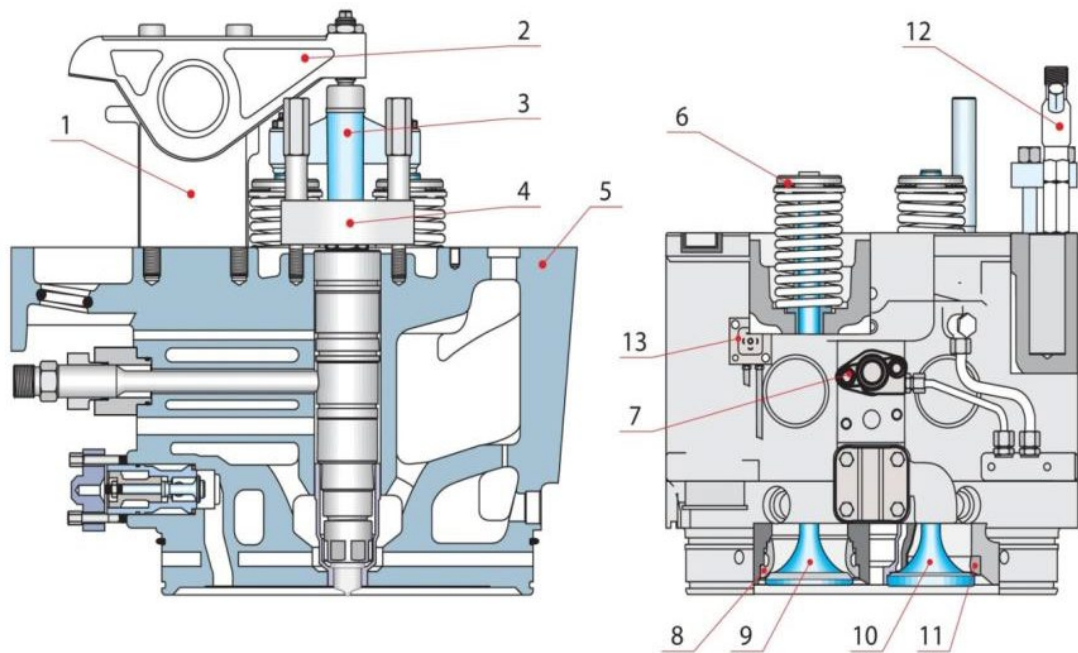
Головка блоку циліндрів: 1 – опірня стійка; 2 – коромисло; 3 – траверса для клапанів; 4 – траверса для форсунки; 5 – корпус головки; 6 – пристрій обертаючий; 7 – гвинти; 8 – сідло випускного клапана; 9 – клапан випускний; 10 – клапан впускний; 11 – сідло впускного клапана; 12 – кран індикаторний; 13 – датчик температури
